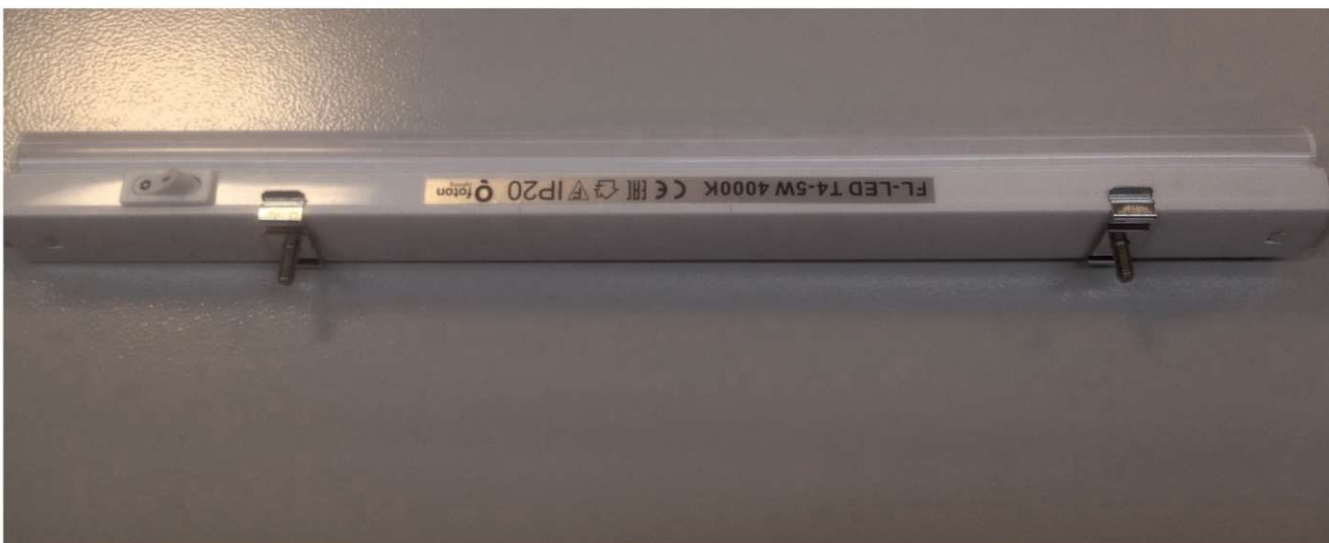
Установка пружинных креплений на корпус светильника.
